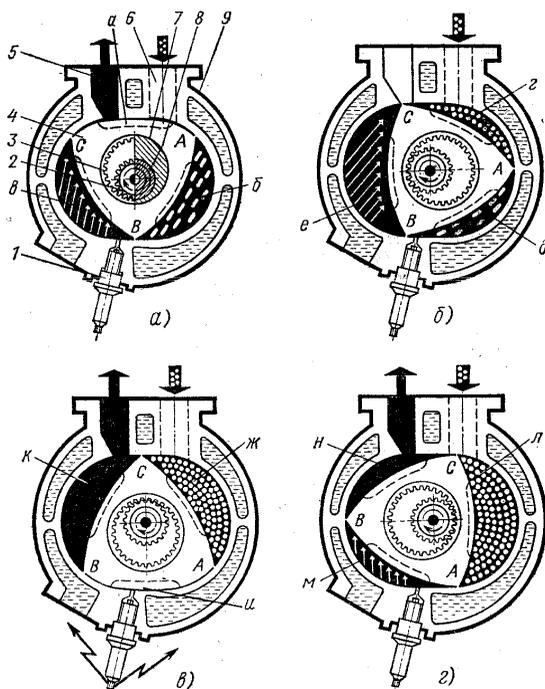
Рабочий цикл роторно-поршневого двигателя
